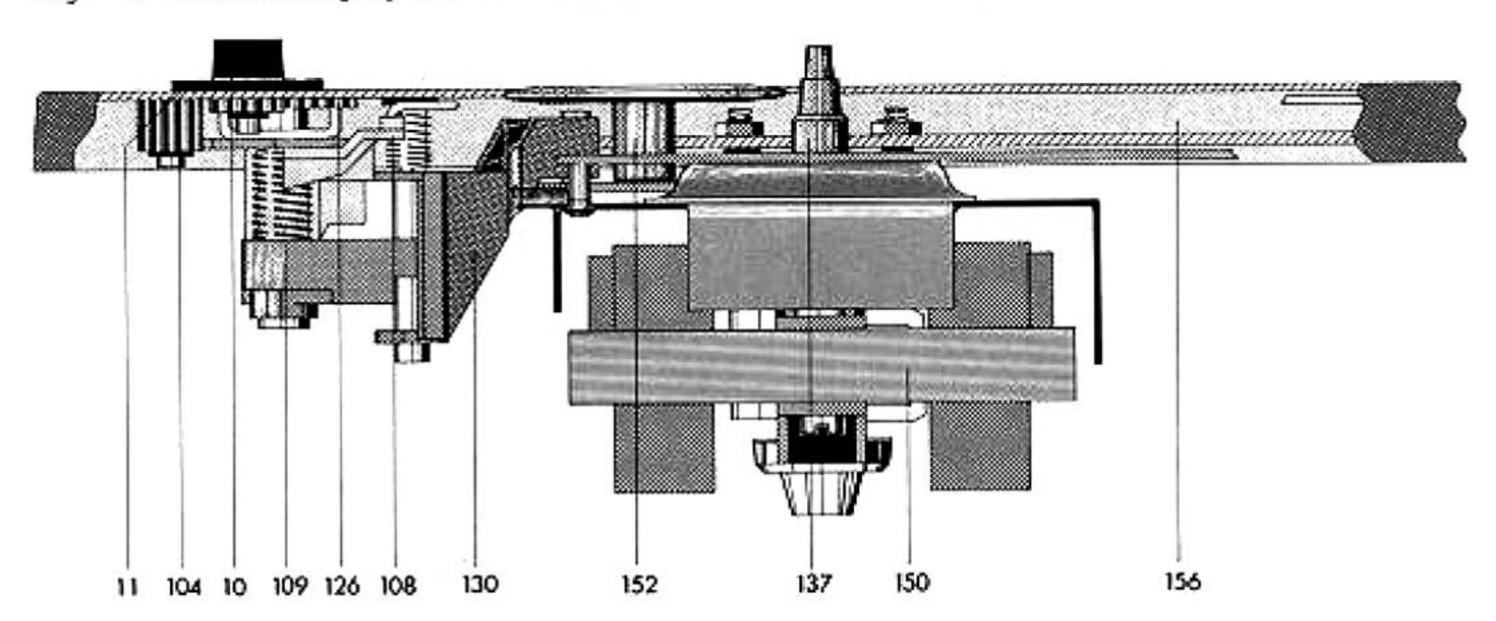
Motoraufhängung und Antrieb des Plattentellers Dust 1222
